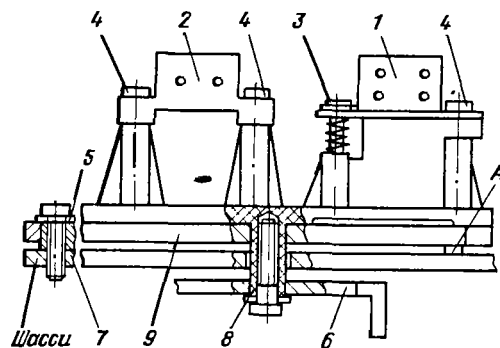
Установка магнитных головок и крепление ползуна ЛПМ
